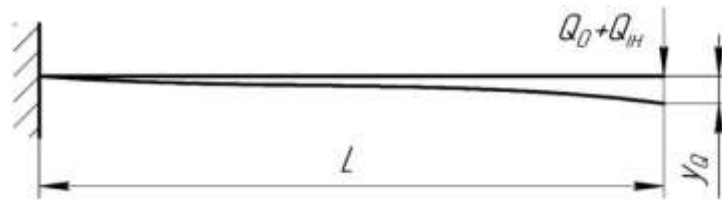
Схематичне представлення циліндричної оправки у формі консольної балки
